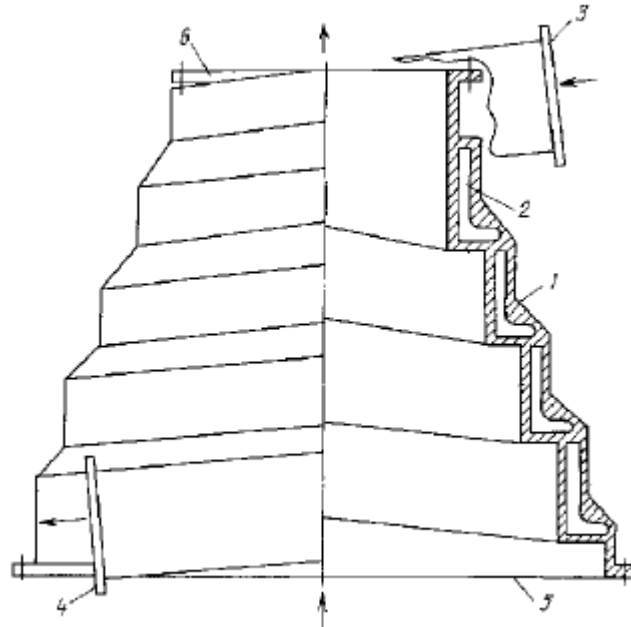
Радиационно-конвективный теплообменник спирального типа :1–корпус; 2– L-образное сечение в корпусе; 3–патрубок подвода нагреваемой среды; 4 –патрубок отвода нагреваемой среды; 5 –подвод греющей среды; 6 – отвод греющей среды
